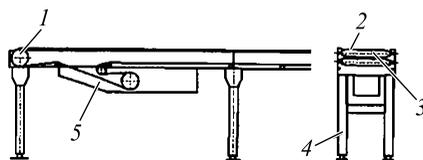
Схема ленточного транспортера: 1 – передний барабан; 2 – лента; 3 – поддерживающие ролики; 4 – несущая конструкция; 5 – привод
